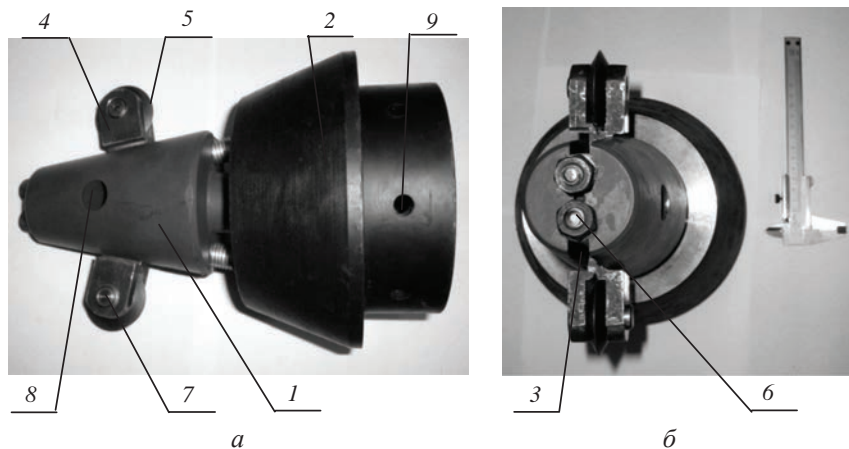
Модель опытного образца рабочего механизма для бестраншейной реконструкции трубопроводов разных диаметров, изготовленная авторами работы по патенту на изобретение РФ № 2359164: *а* — вид сбоку; *б* — вид спереди; 1 — режущая головка; 2 — расширитель для увеличения диаметра скважины; 3 — фигурный паз; 4 — вилка; 5 — дисковый нож; 6 — регулировочный винт; 7 — ось; 8 — отверстие для крепления тягового элемента; 9 — отверстие для крепления нового трубопровода
